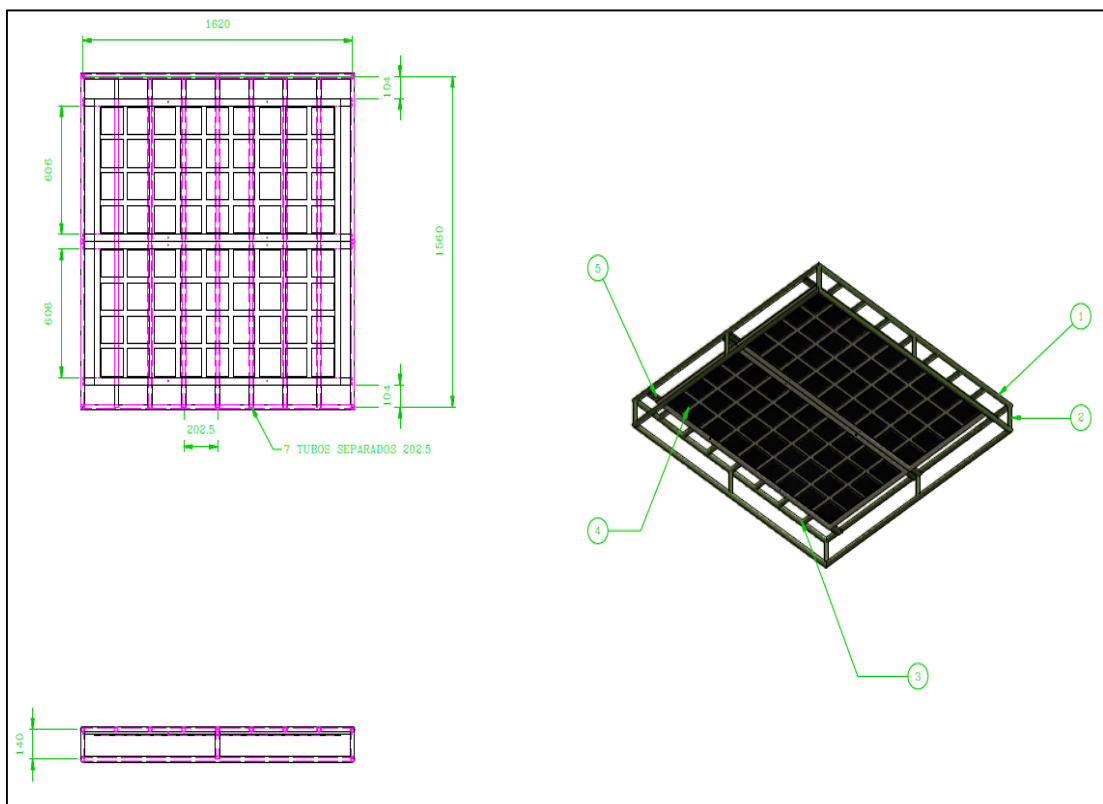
Plano de la estructura tipo parrilla con paneles solares para la construcción del sistema
